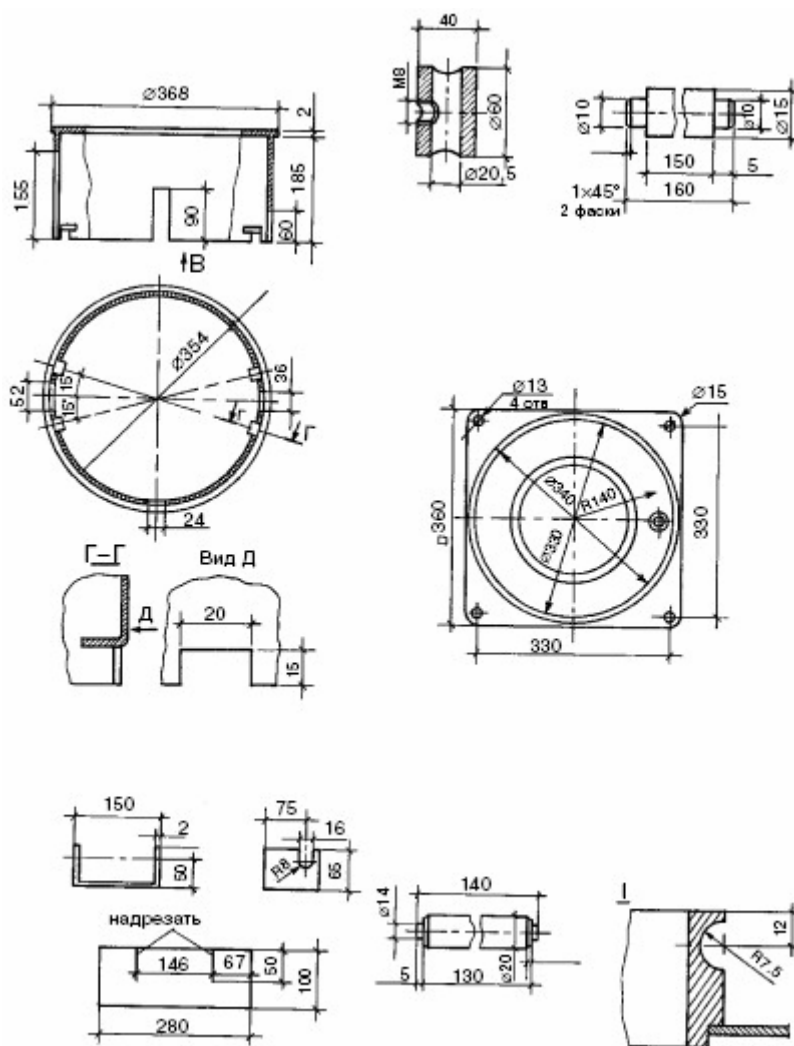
(продолжение). Конструктивная схема водоподъемника: 1 – кожух приводного механизма; 2 – втулка стойки вала; 3 – пластина стабилизатора; 4 – труба стабилизатора; 5 – основание; 6 – вал; 7 – опорный ролик; 8 – корпус приводного механизма; 9 – приводной ролик; 10 – лента-транспортер; 11 – натяжной механизм; 12 – стяжной валик; 13 – рамка основания; 14 – обойма отжимного устройства; 15 – противовес; 16 – ось обоймы отжимного устройства; 17 – водоприемник; 18 – сливной штуцер; 19 – ось стяжного валика
